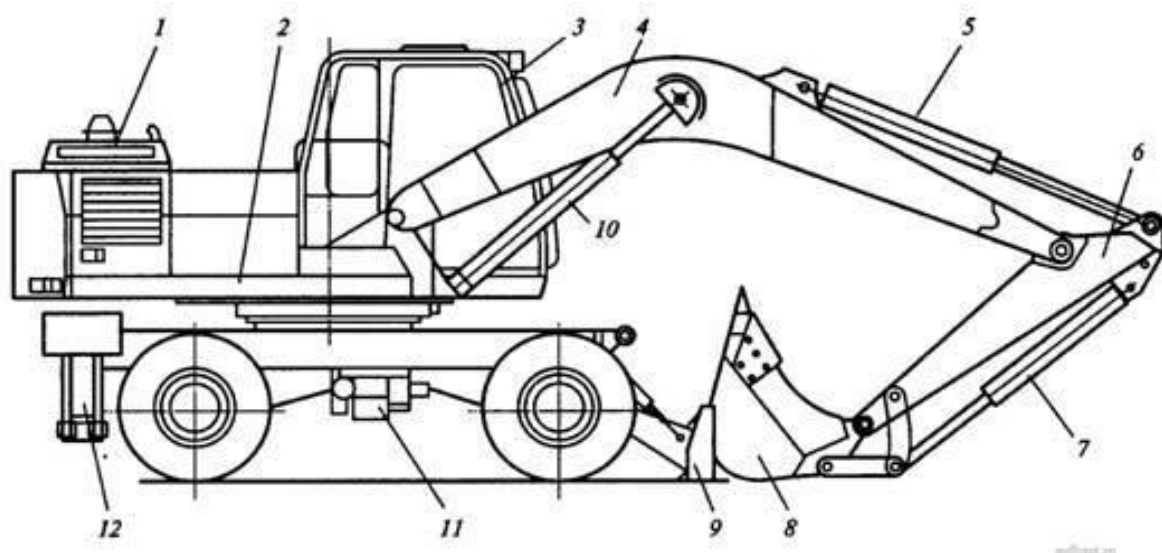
Экскаватор ЕК-18 вид сбоку: 1 - силовая установка; 2 - поворотная платформа; 3 - кабина оператора; 4 - моноблочная стрела; 5, 7, 10 - гидроцилиндры рукояти, ковша и стрелы; 6 - рукоять; 8 - ковш; 9 - опора-отвал; 11 – пневмокошесное ходовое устройство; 12 - выносная опора.
